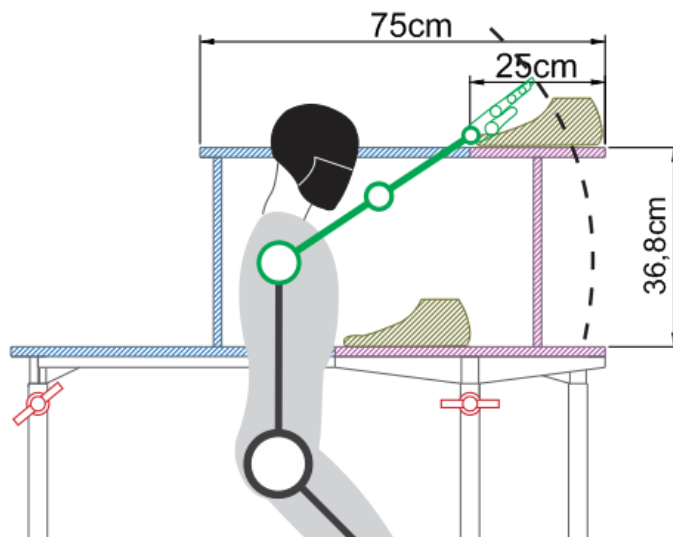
Vista perfil del desplazamiento de la nueva estación, montado 2
